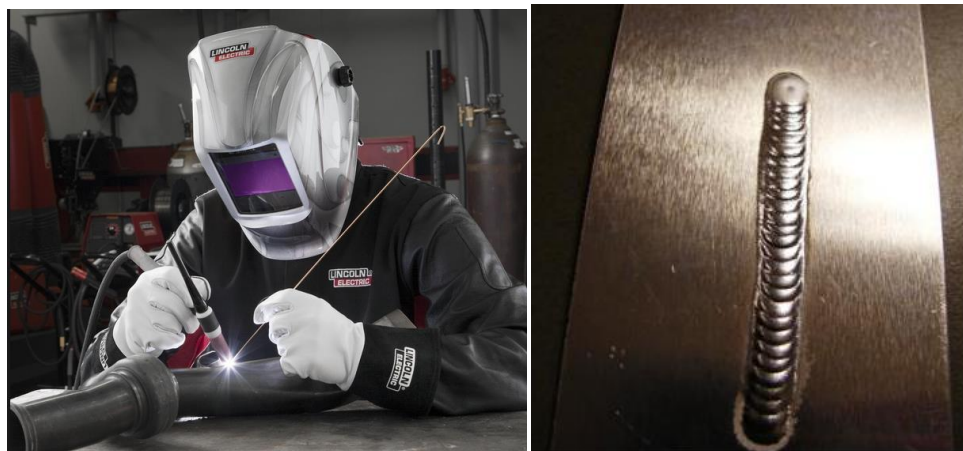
Soldadura de arco de tungsteno protegida con gas
